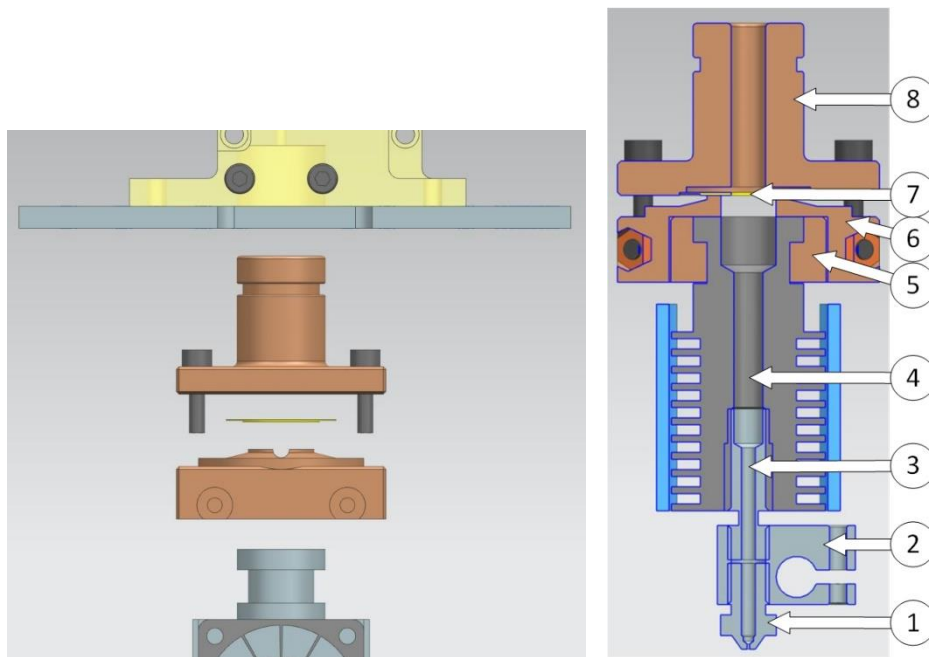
Explosions- und Schnittansicht der Variante A zwischen Cold- und Hot End
